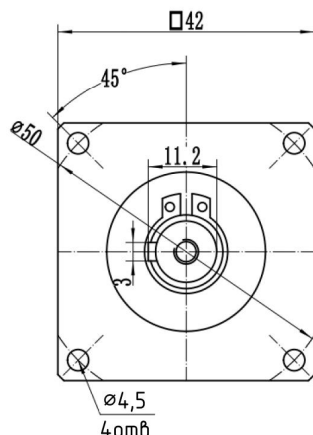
Габаритные и присоединительные размеры редуктора РП042Ф-ХХ-5-22
